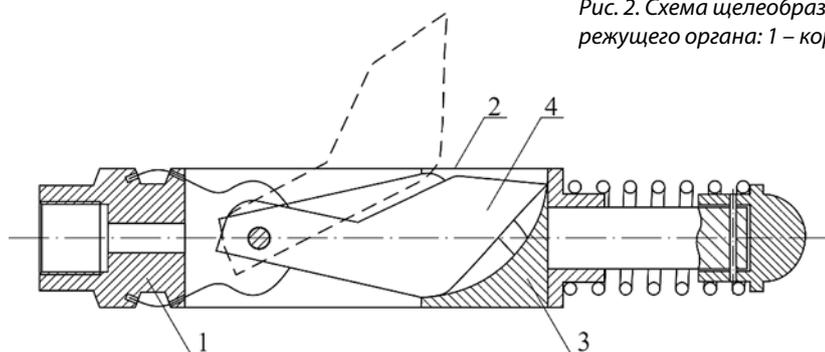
Схема щелеобразователя с механическим перемещением режущего органа: 1 – корпус; 2 – продольные окна; 3 – шток; 4 – режущий орган
